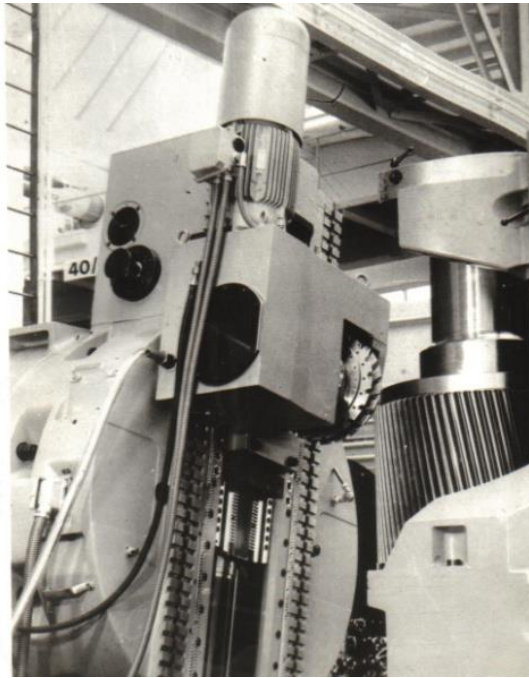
Спеціальний супорт до зубостругального верстата з дисковими твердосплавними фрезами фірми «МООГ» (Швейцарія)
